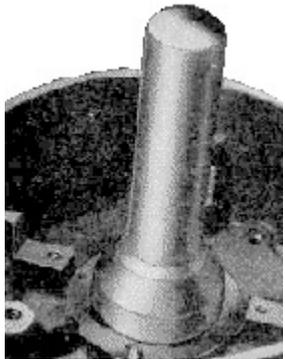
Einsetzen des Ringrillenslagers 6205 mit dem Dorn 05 MW 12-4
